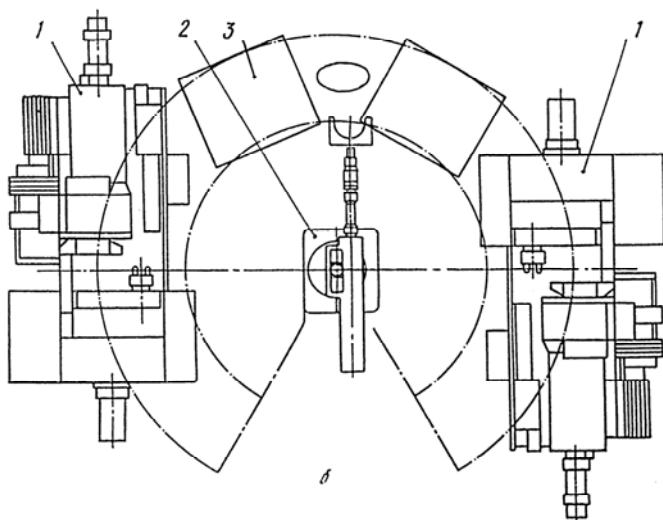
Схема РТК с параллельным расположением токарных станков:
